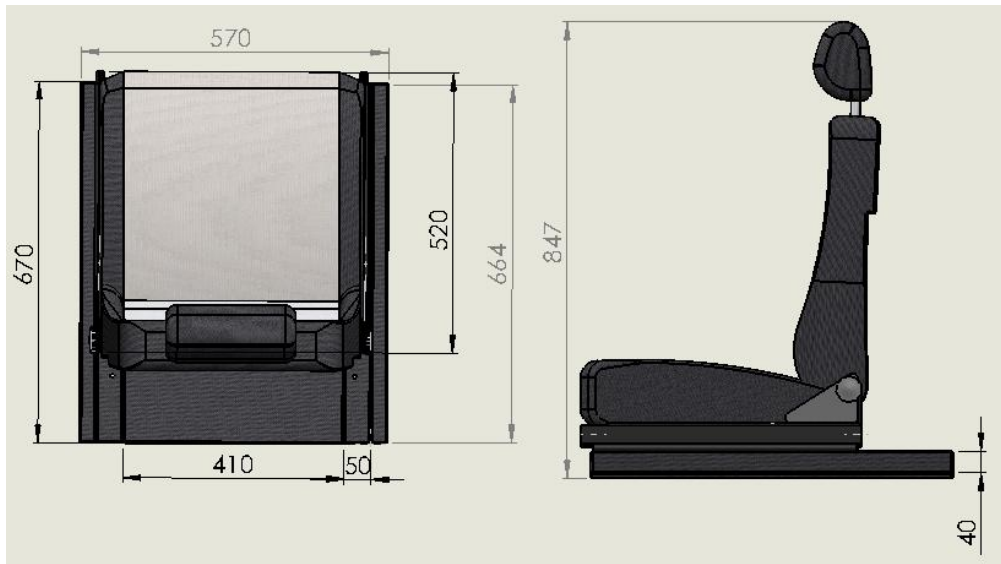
Dimensiones principales asiento Audi A4. Cotas en milímetros
